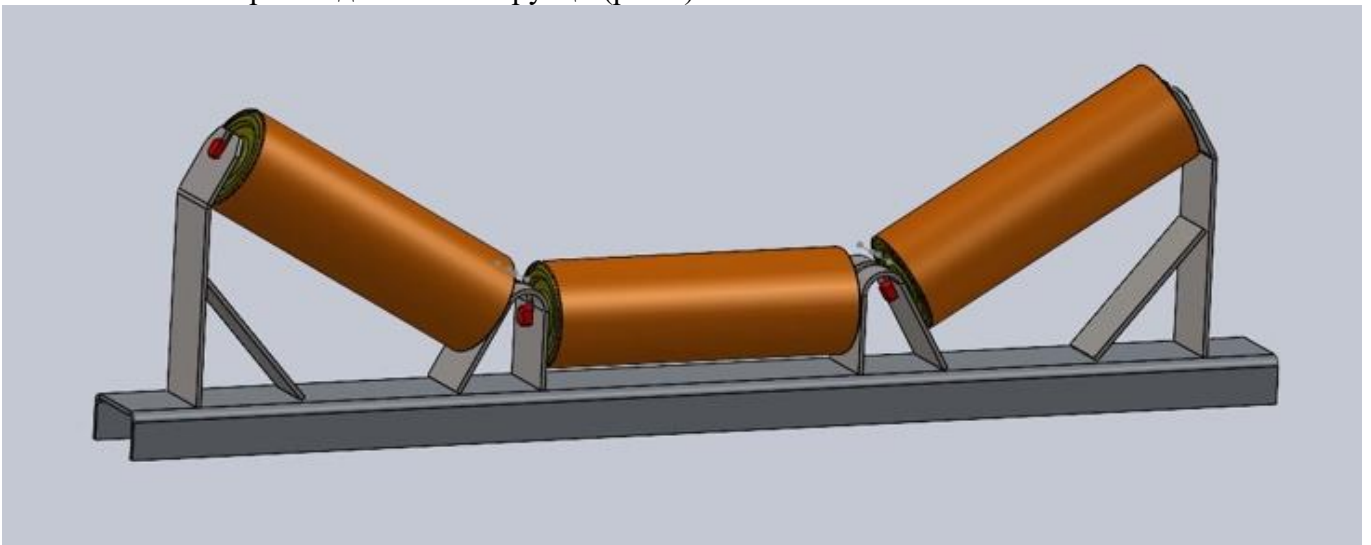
Стандартна роlikоопора стрічкового конвеєра
